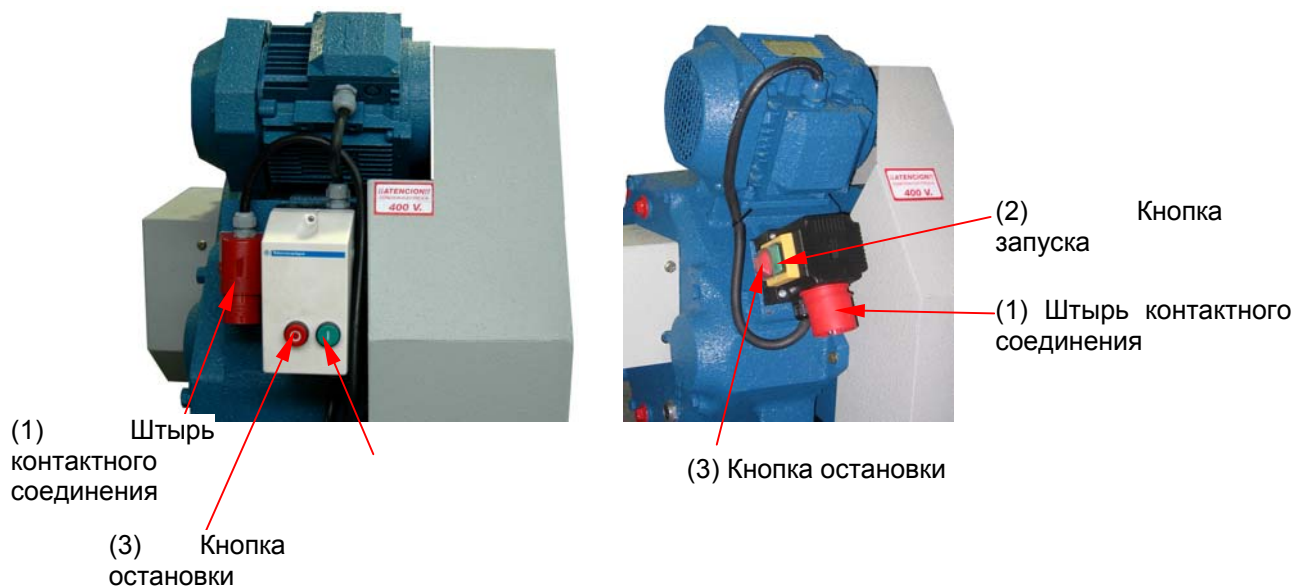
Коннектор, аварийный выключатель для защиты двигателя и электропитание
